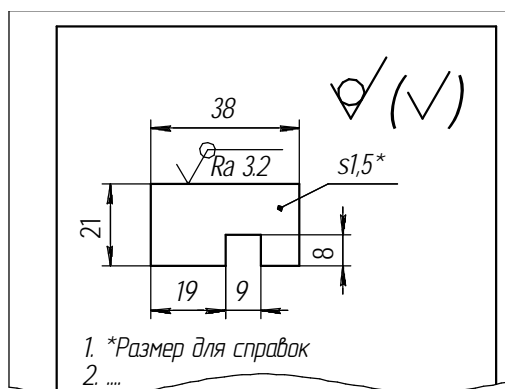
Чертеж детали с одинаковой шероховатостью поверхностей, образующих контур
